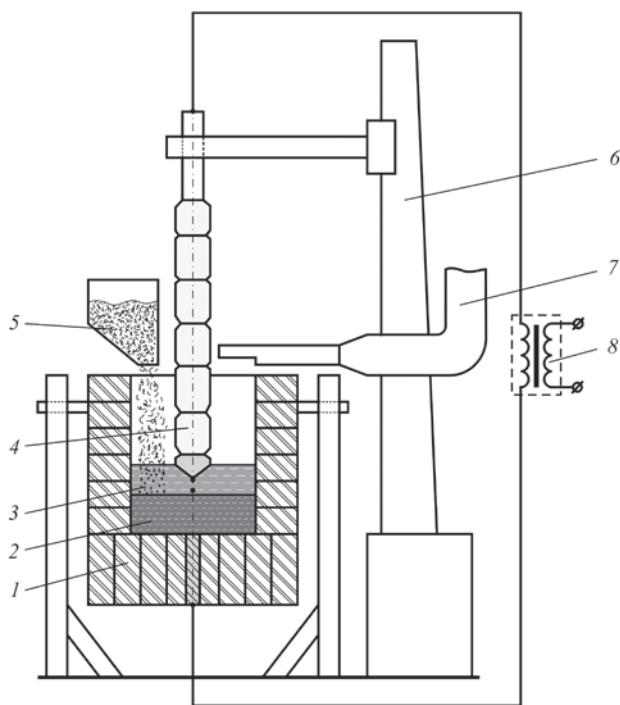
Схема переробки нержавіючої стружки способом електрошлакової тигельної плавки: 1 — тигель; 2 — металева ванна; 3 — шлакова ванна; 4 — витратний металевий електрод; 5 — бункер із шихтою; 6 — направляюча колона з пересувним механізмом; 7 — патрубок системи газовідведення; 8 — джерело живлення
